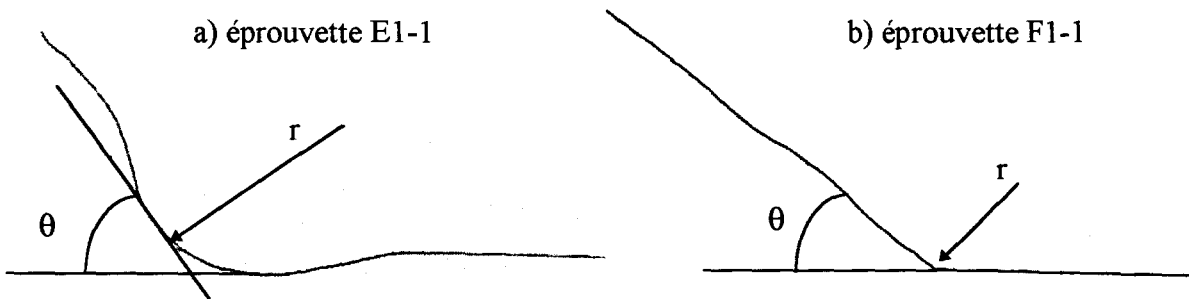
Profils du pied de cordon dans le cas soudage MAG+meulage (a) et soudage Innershield (b)
